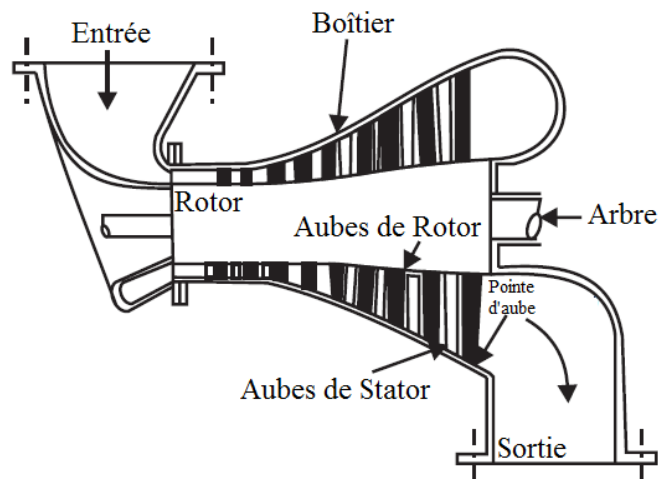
Vue en coupe d'une turbine montrant les principaux composants de la turbomachine [30]
